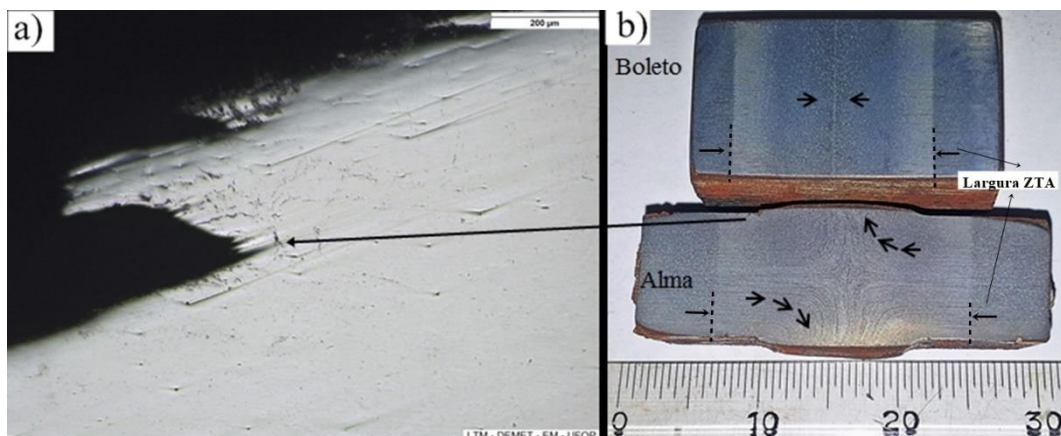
(a) Concentrador de tensão na alma de trilho soldado por centelhamento no final do corte de rebarba. (b) Padrão de deformação devido ao processo de soldagem na alma e no bolete (setas), retivo de iodo. Seção (b) da Figura 4.6.
